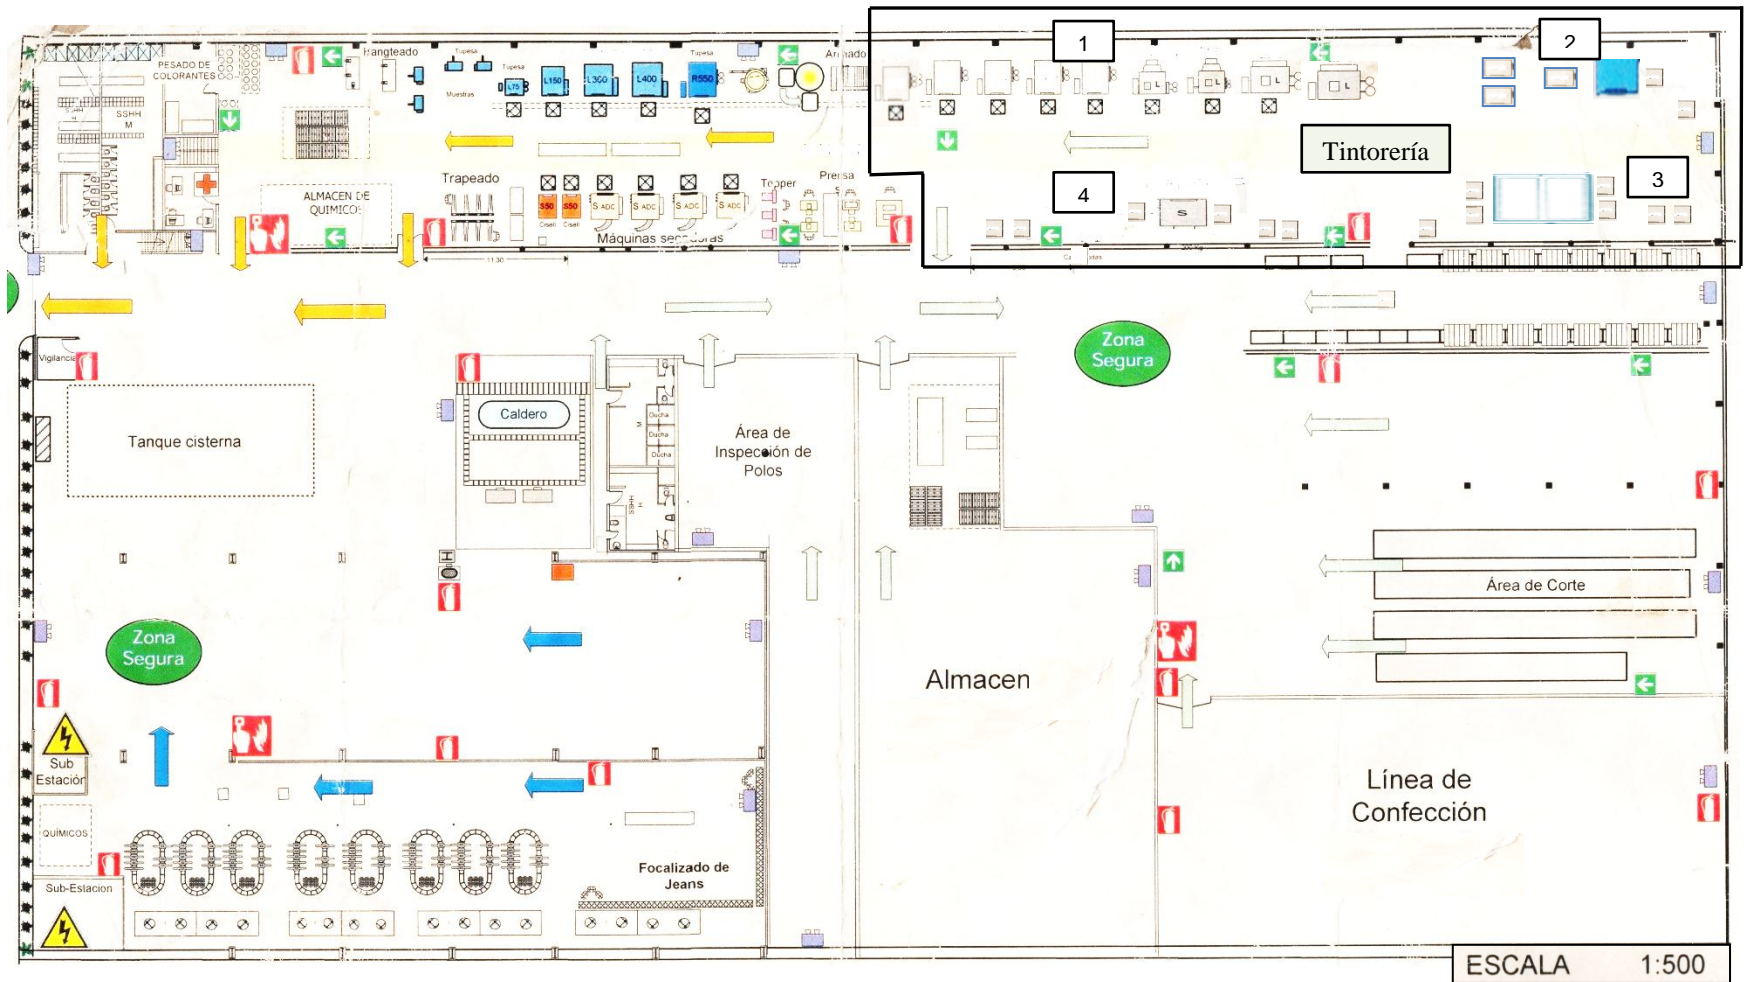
Distribución de máquinas en la planta ST01. Tintorería: 1000 m²
